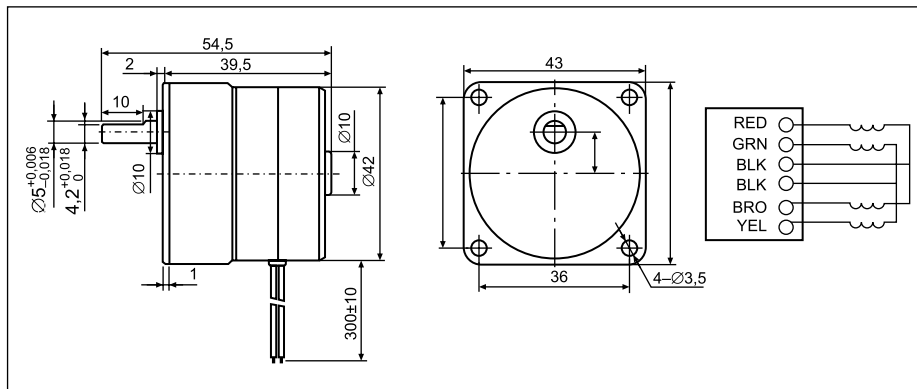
Габаритный чертеж и схема подключения обмоток шагового двигателя серии MT17FJ
